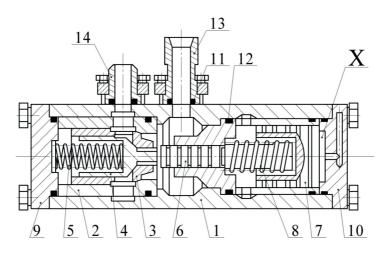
Гидрозамок двухстороннего действия: 1 – корпус; 2 – седло; 3 – клапан; 4 – декомпрессор; 5 – пружина; 6 – золотник; 7 – золотник-поршень; 8 – пружина; 9, 10 – крышки; 11, 12 – кольца; 13, 14 – штуцеры
